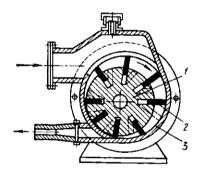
Схема ротационного компрессора: 1 – ротор; 2 – лопасти; 3 – корпус
